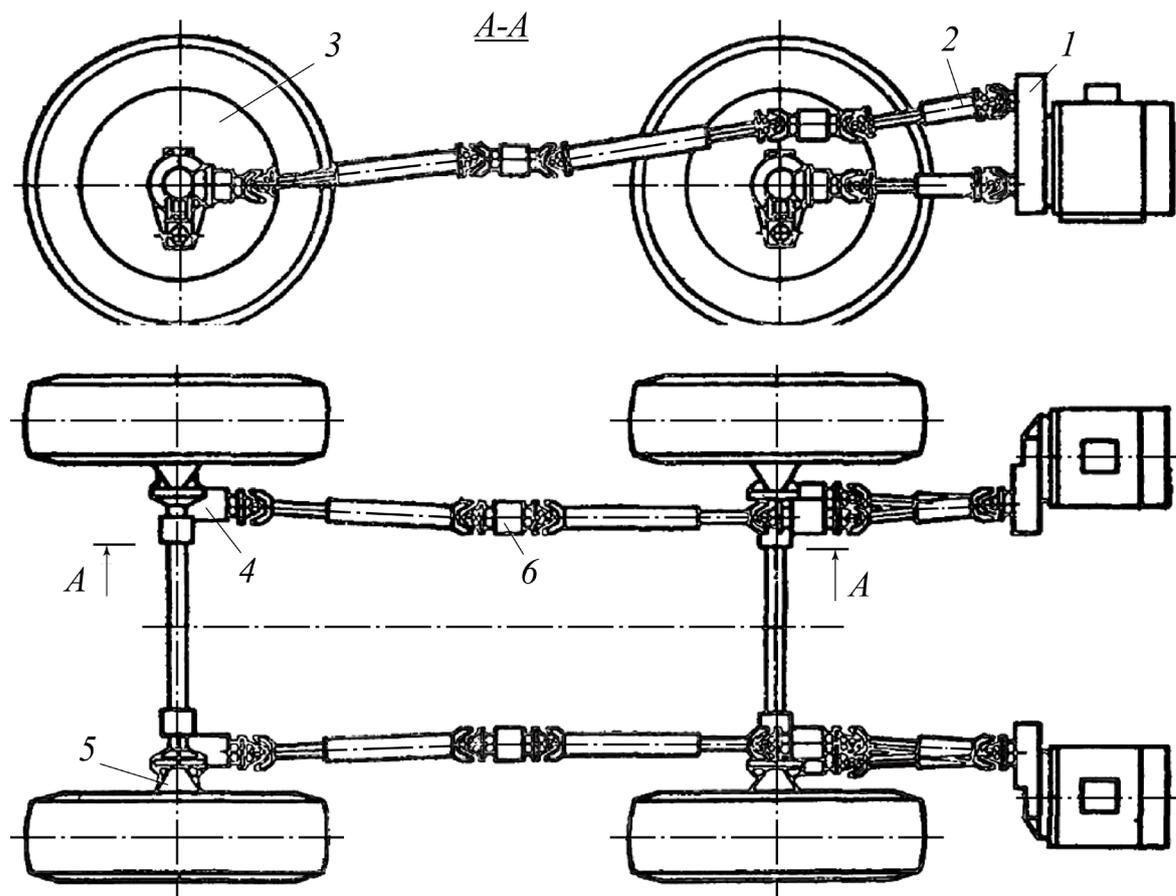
Схема компоновки трансмиссии привода ходовой части: 1 – редуктор ходовой части; 2 – карданная передача; 3 – колесный планетарный редуктор; 4 – угловой редуктор; 5 – шарнир равных угловых скоростей; 6 – промежуточная опора
